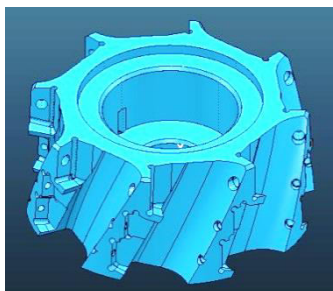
Модель корпусу РІ, імпортована в Powermill
